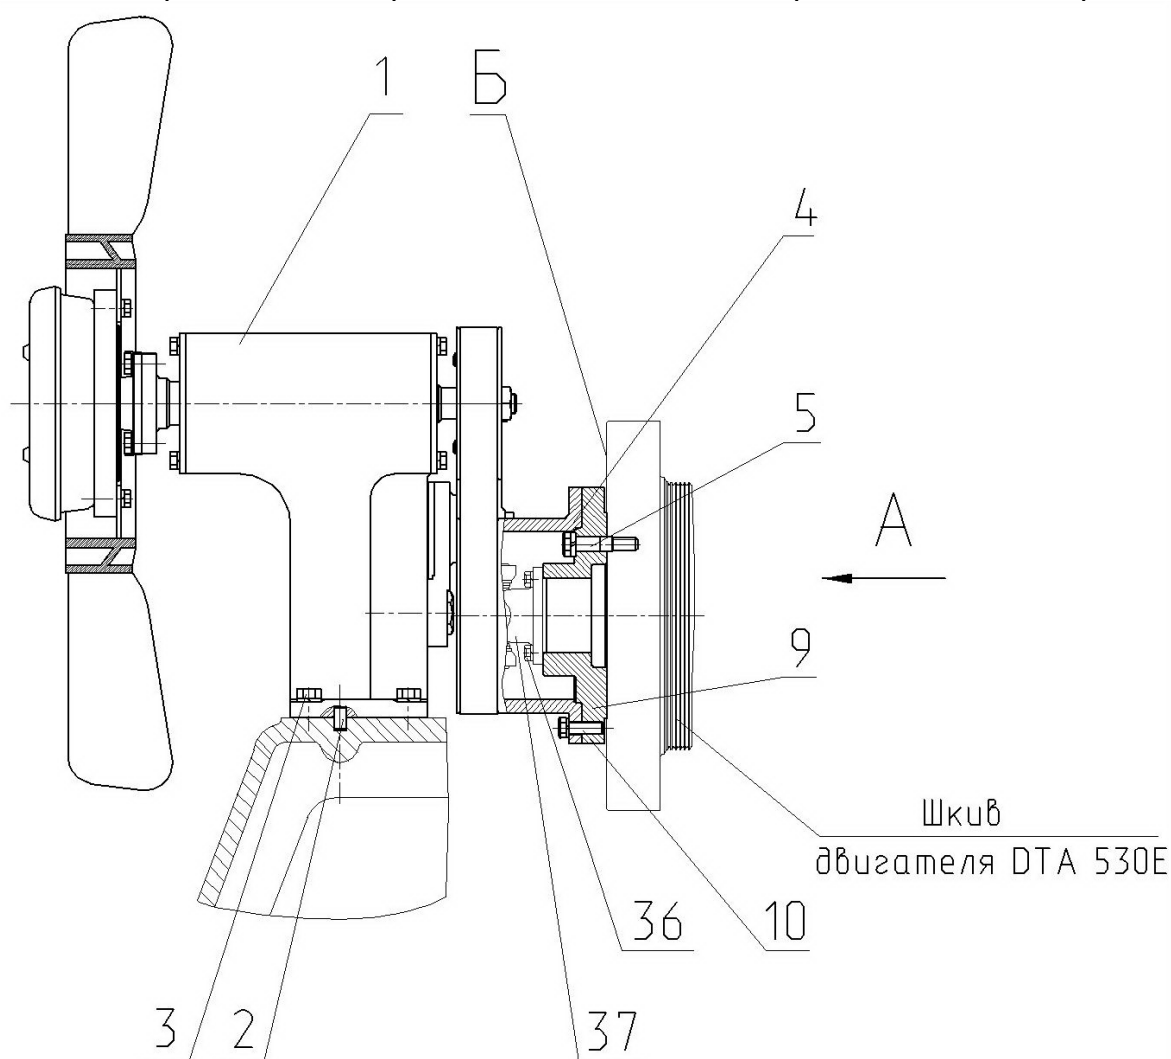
Привод вентилятора на двигателе DETROIT DIESEL.
